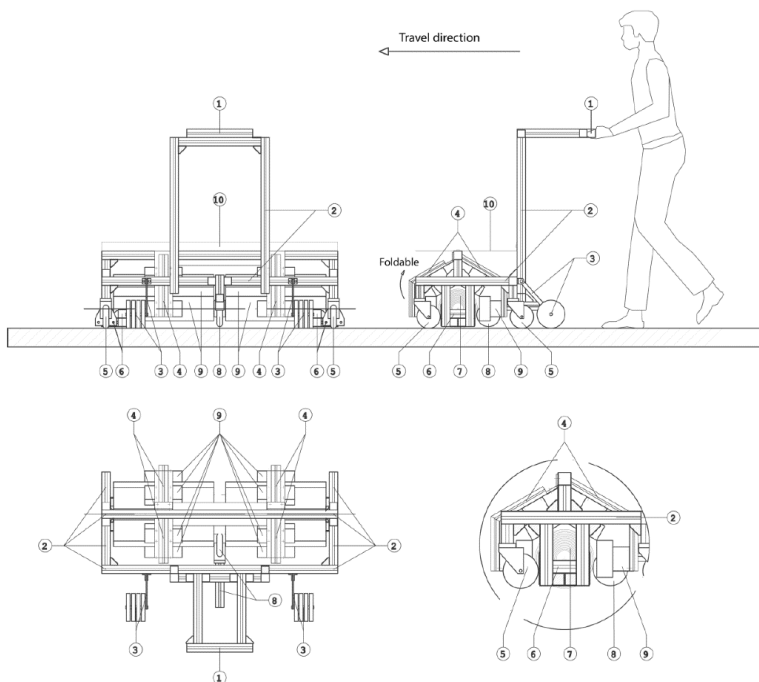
Ортогональні види конструкції: 1 – ручки, 2 – конструкція візка, 3 – барабанні ролики, 4 – конструкція нагрівачів, 5 – колеса, 6 – боковини обмежувача валку, 7 – асфальтовий валок, 8 – допоміжне колесо, 9 – нагрівачі та 10 – кришка корпусу
